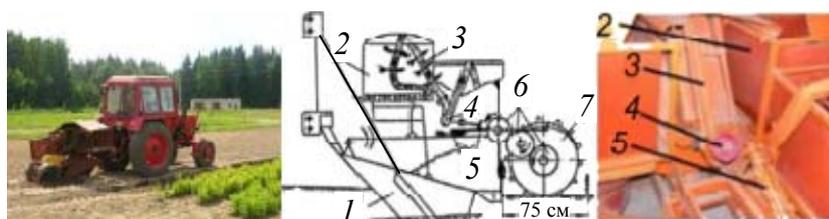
Схема лесопосадочной автоматической машины МЛА-1А: 1 – сошник; 2 – контейнер с заряженной кассетой; 3 – кассетный сеянцедержатель; 4 – кассетопротяжный механизм; 5 – захват; 6 – зубчатая передача; 7 – приводной и прикатывающий катки
